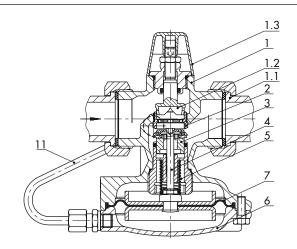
Typ 45-9 mit Anschweißenden
